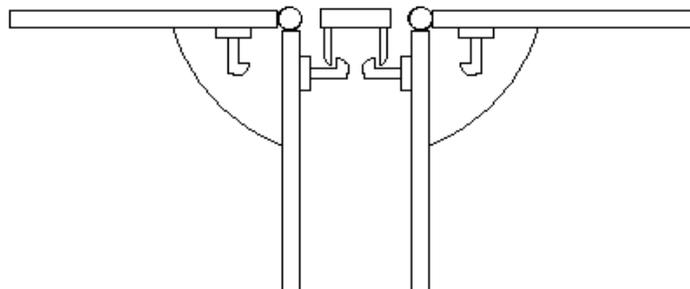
Detalle del corte transversal de la zona remarcada en la Fig.1.1.
